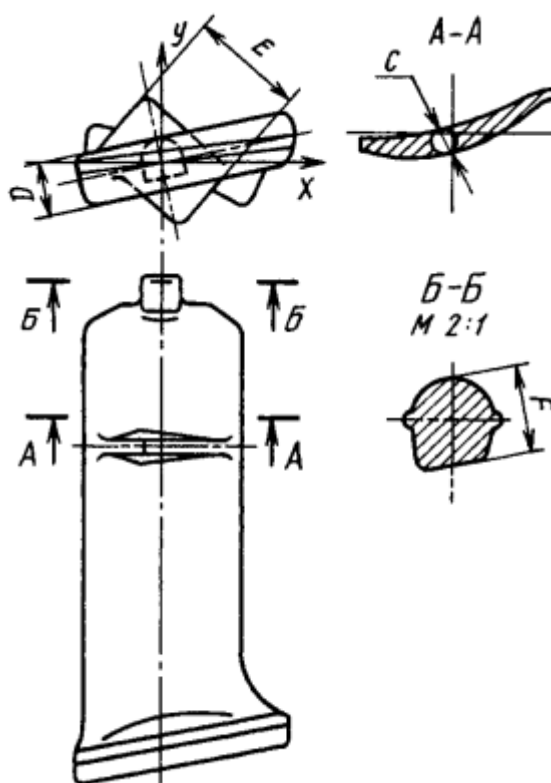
Заготовка робочої лопатки компресора з антивібраційною полицею
